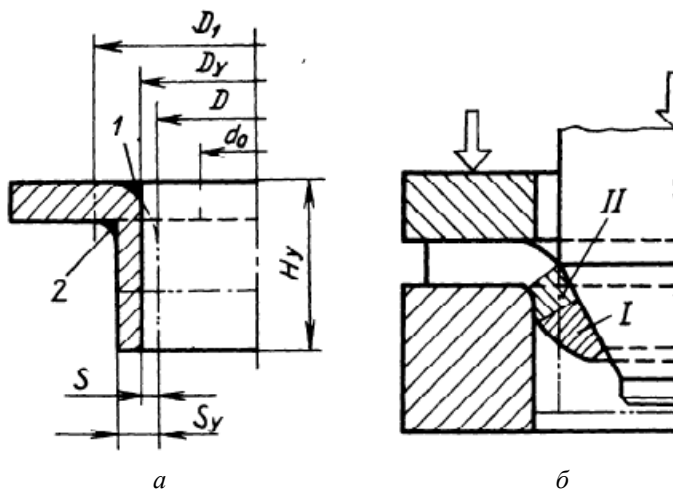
Деталь, получаемая отбортовкой с утонением (а), схема отбортовки (б)
